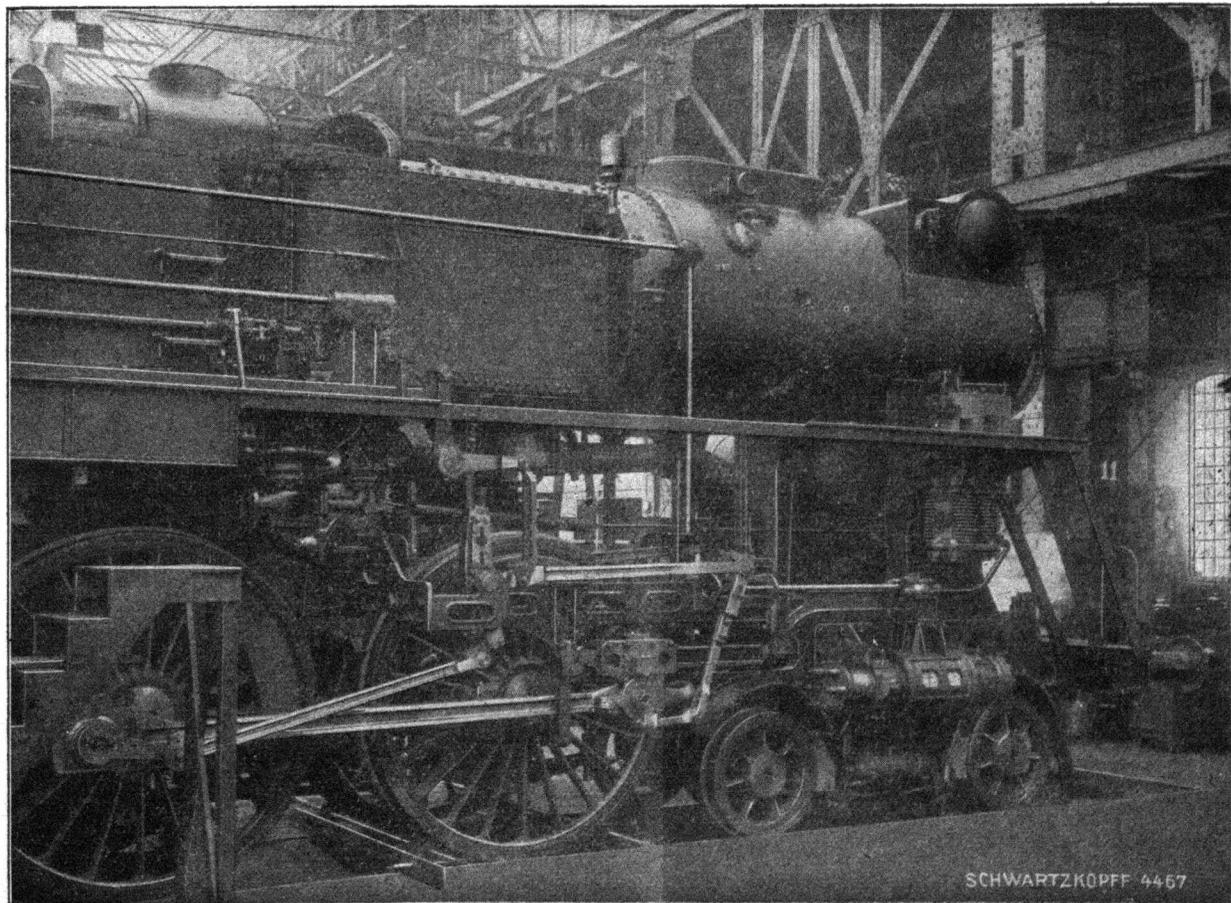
Verbindung von Luftvorwärmer, Rauchkammer (ohne Umwälzpumpen), Niederdruck-Wärmeaustauscher und Vorkammer.
